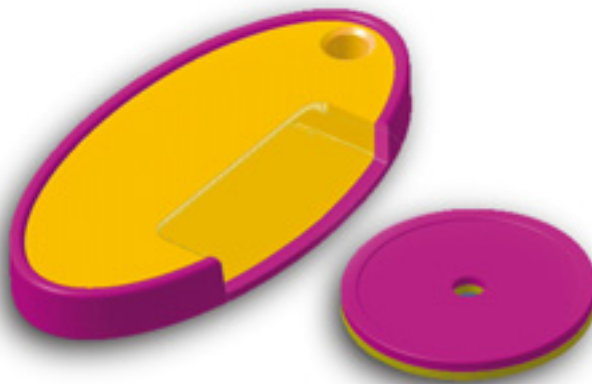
Einkaufswagenchip mit Chipaufnahme [13.17, 13.21]
